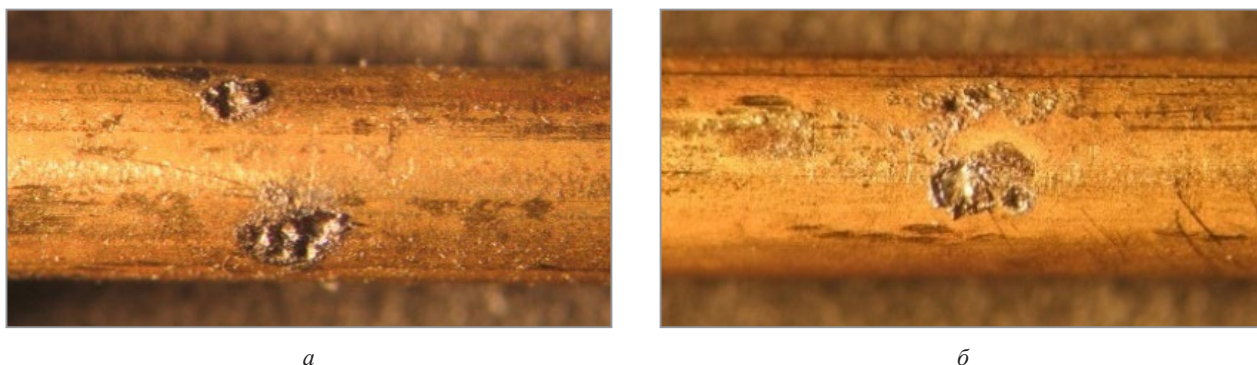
Внешний вид поверхностных дефектов типа «прижог от искрения» на латунированной проволоке-заготовке. х9
